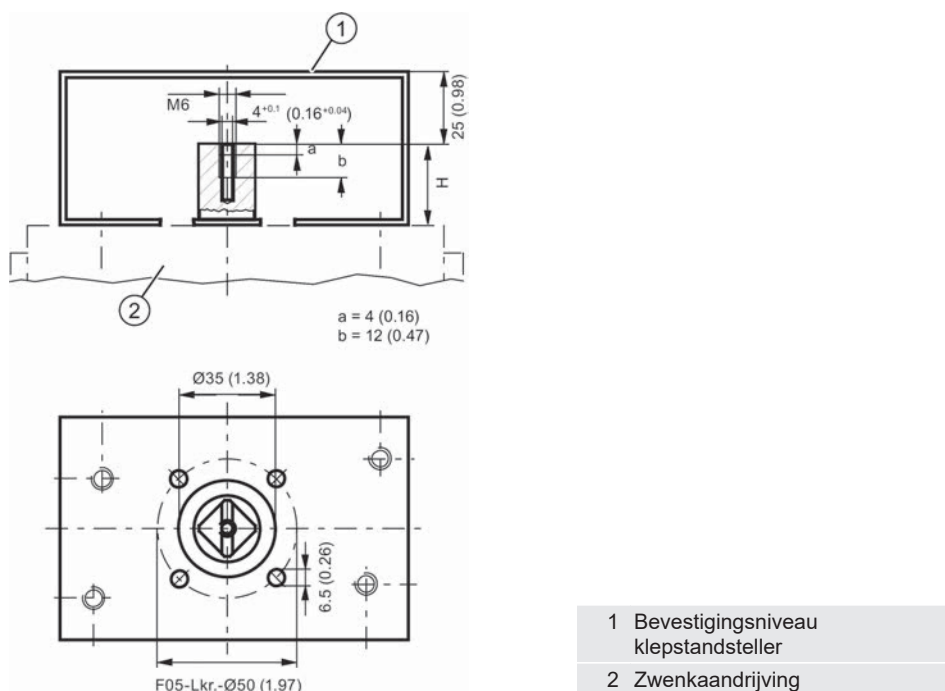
Montageconsole (levering fabrikant van de aandrijving) en maten
